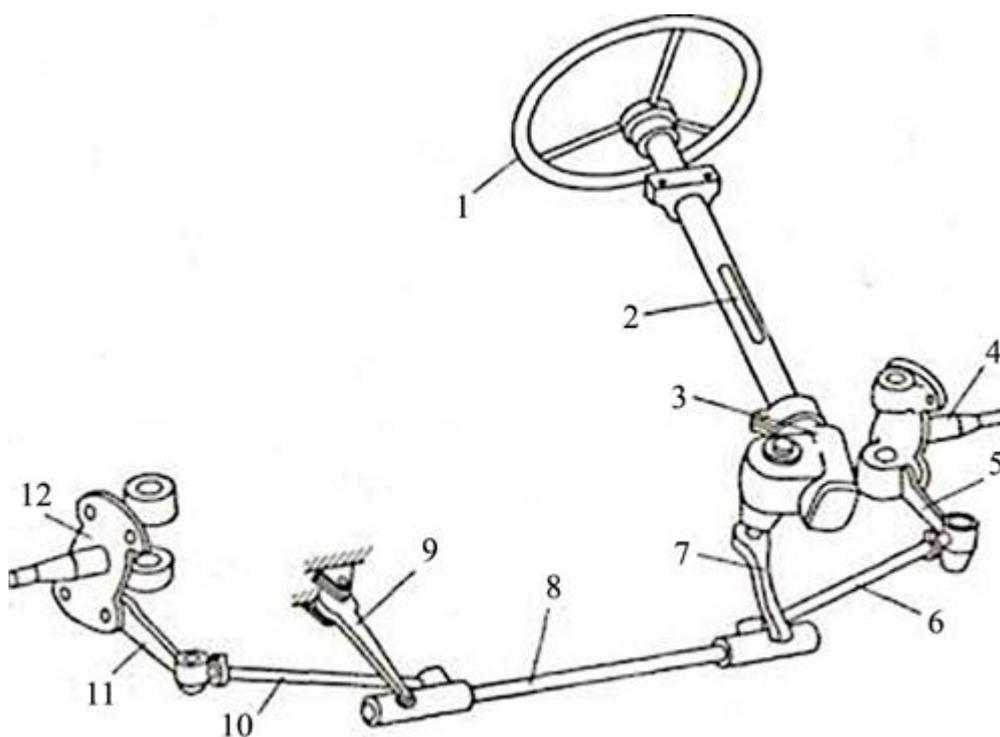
Рулевое управление легкового автомобиля. 1 – рулевое колесо; 2 – вал руля; 3 – рулевая передача; 4,12 – поворотная цапфа; 5,9,11 – рычаги; 6,8,10 – приводы (тяги); 7 – рулевая сошка.
